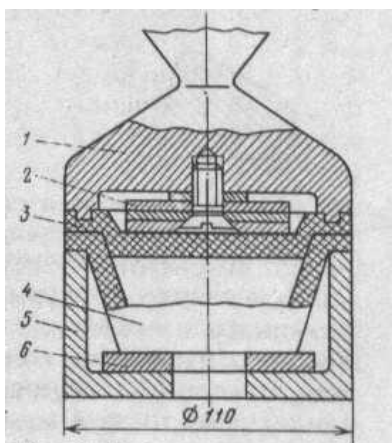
Схема сварки цилиндрического изделия контурным волноводом с акустическим экраном: 1 - контурный волновод; 2 - звукопоглощающие пластины; 3 - крышка изделия; 4 - банка; 5 - стакан-опора; 6 - подложка
